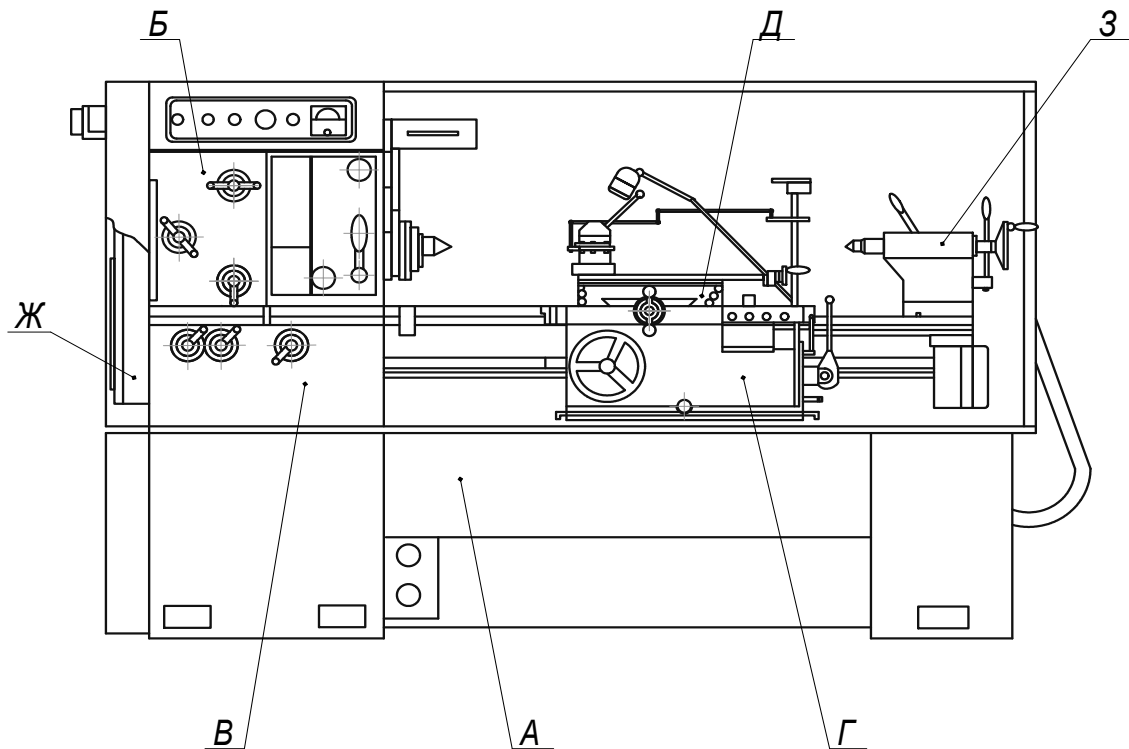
Расположение составных частей станка модели 16Д25
